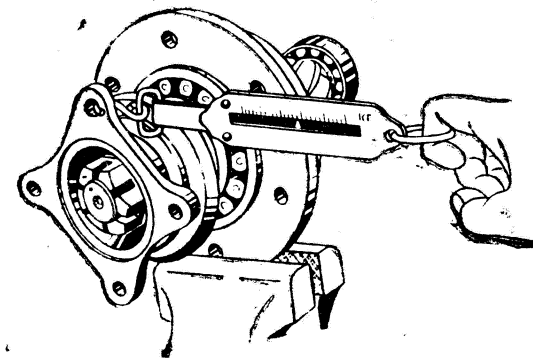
Проверка затяжки подшипников ведущей шестерни.
